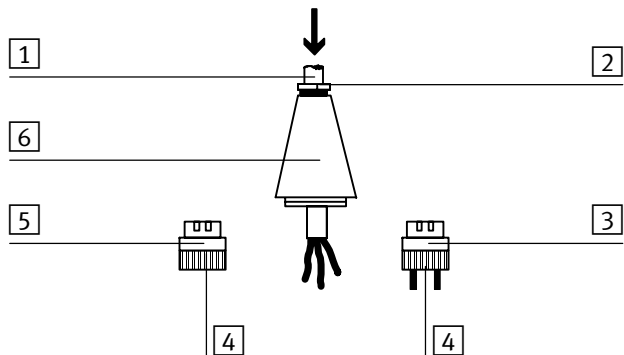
/1: Stecker-/Dosen-Einzelteile und Kabeldurchführung
